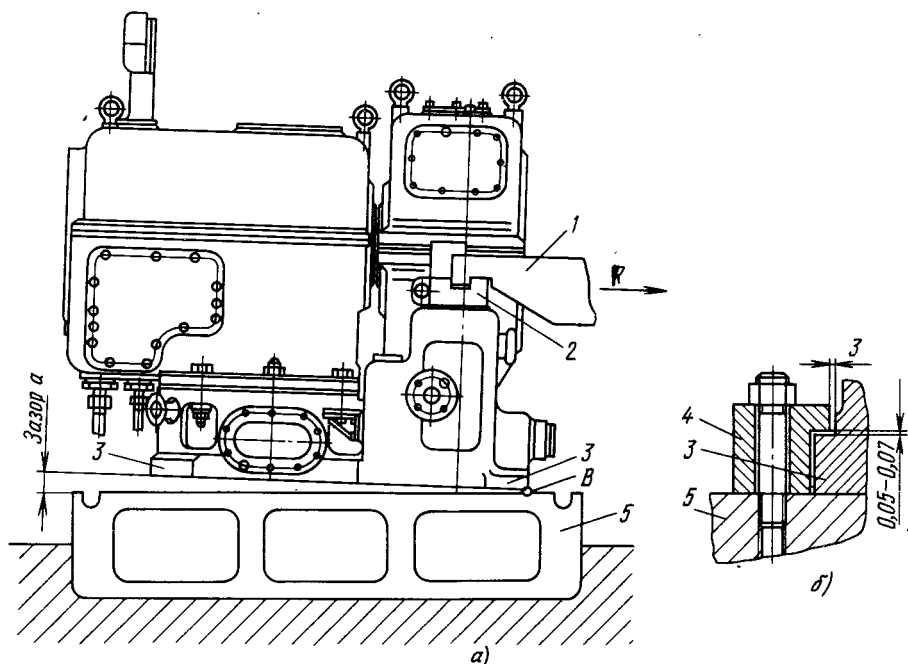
Крепление корпуса подшипника к фундаментной раме:
